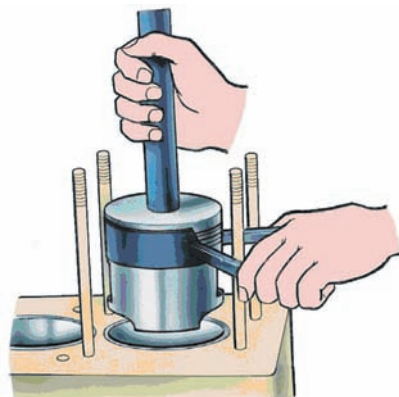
Пристосування для установки поршня з кільцями в циліндр
